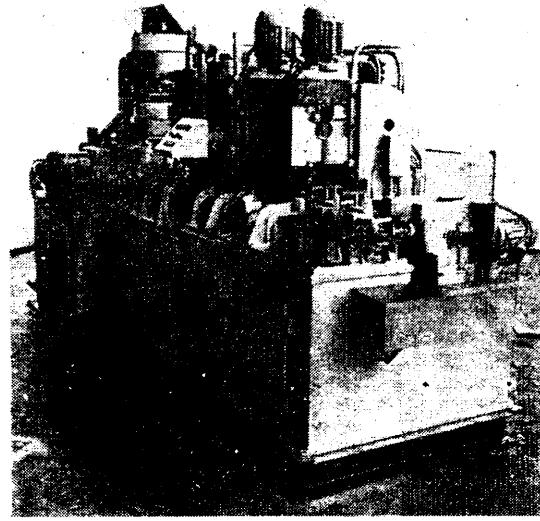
Автоматическая линия сборки и частичной механической обработки шатуна двигателя производительностью 300 шт. в час
